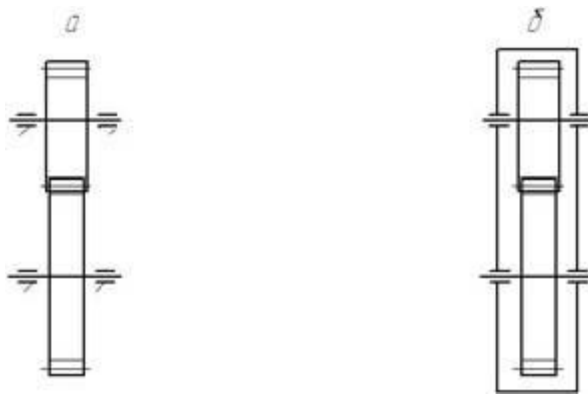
Схеми передавачів за конструкцією корпусу
